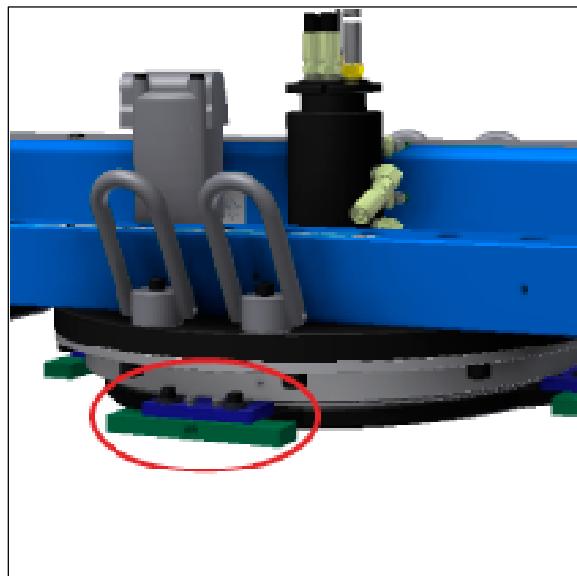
Блоки, крепящиеся прихваточными сварными швами к удлинительным плитам
